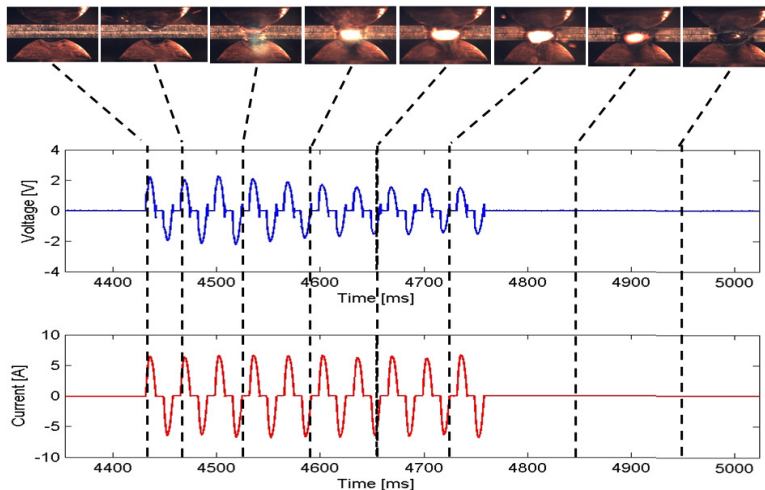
Filmagem do processo de soldagem utilizando dez ciclos
